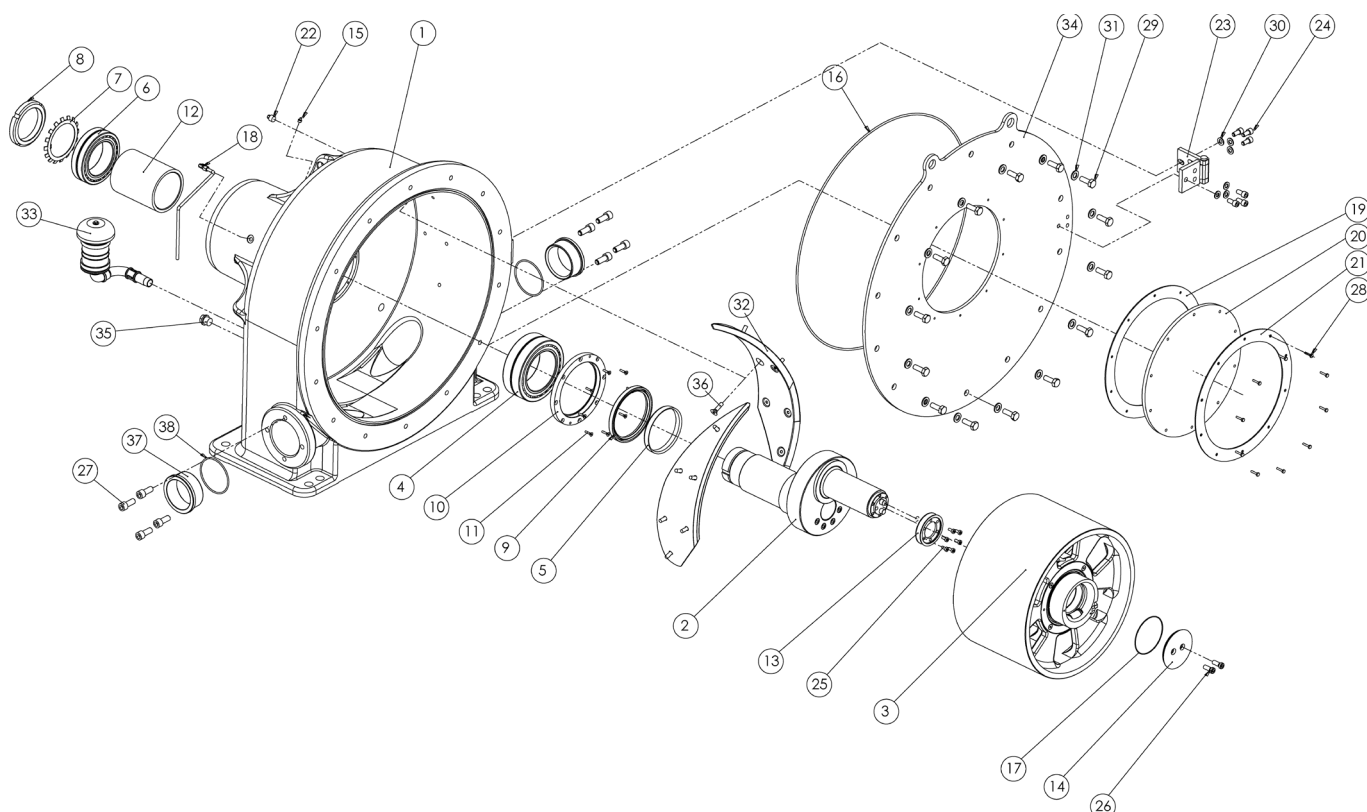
Vista de despiece del cabezal de la bomba LPP-T
